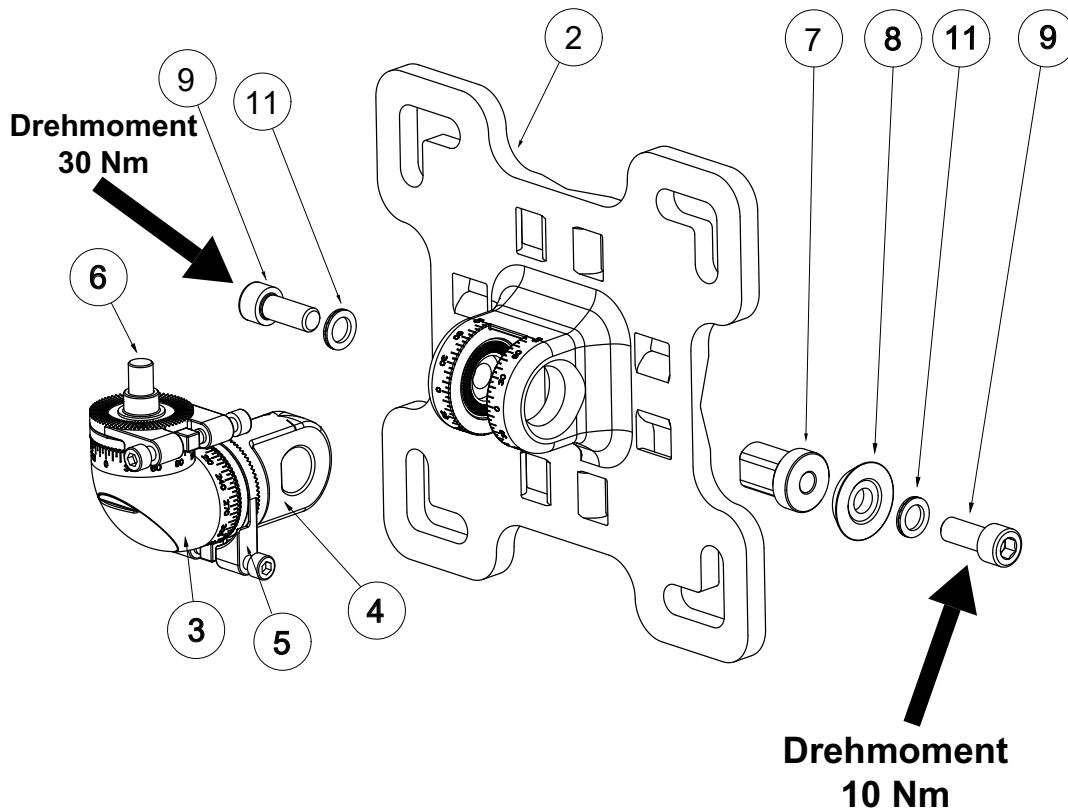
Wechseln des Montageplattenadapters für die universelle Montagehalterung
